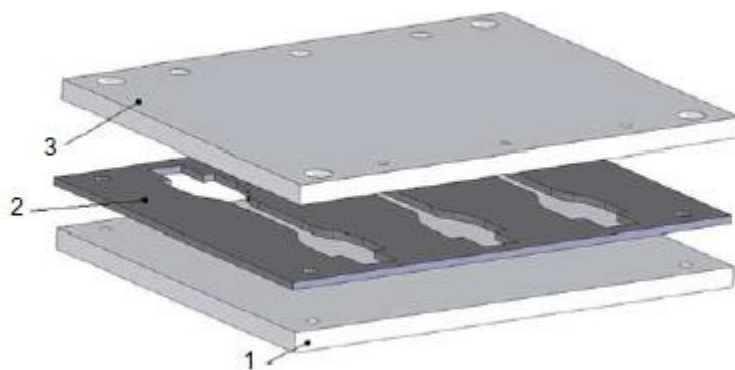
Molde de para fabricação de provetes em adesivo maciço [29]
